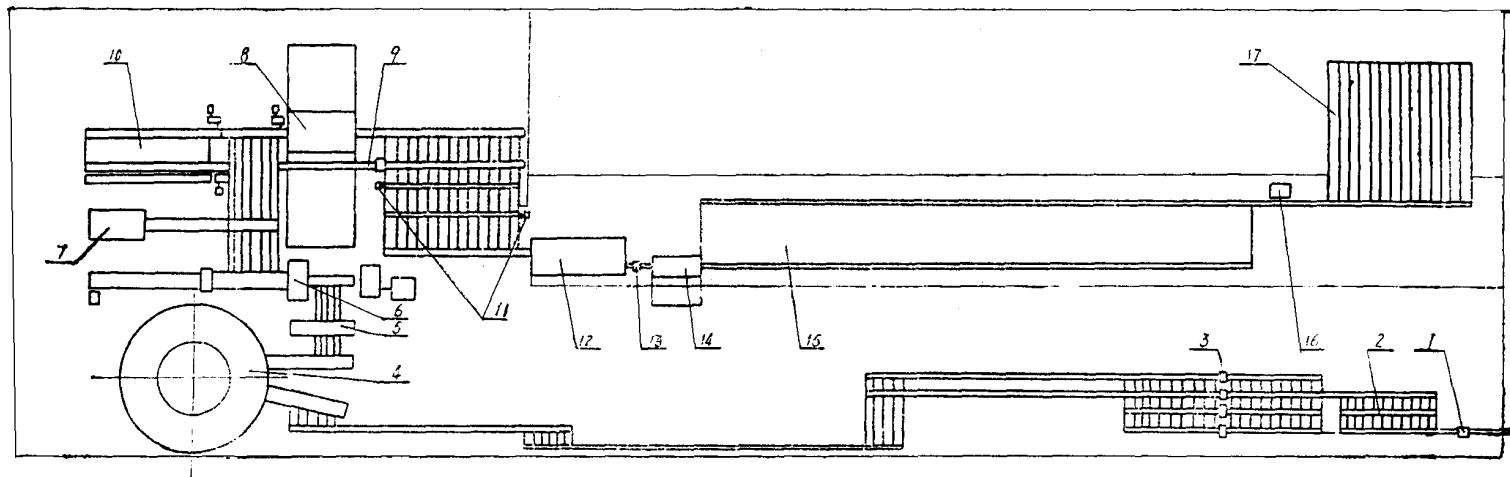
英国温斯菲尔德厂连轧管机组平面图
